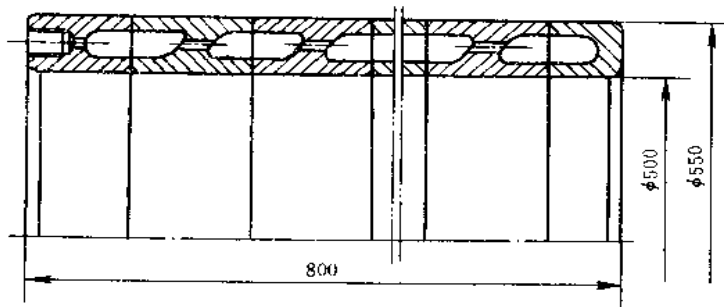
焊接成的液压胀套（应用于大型剪床的传动装置中）
